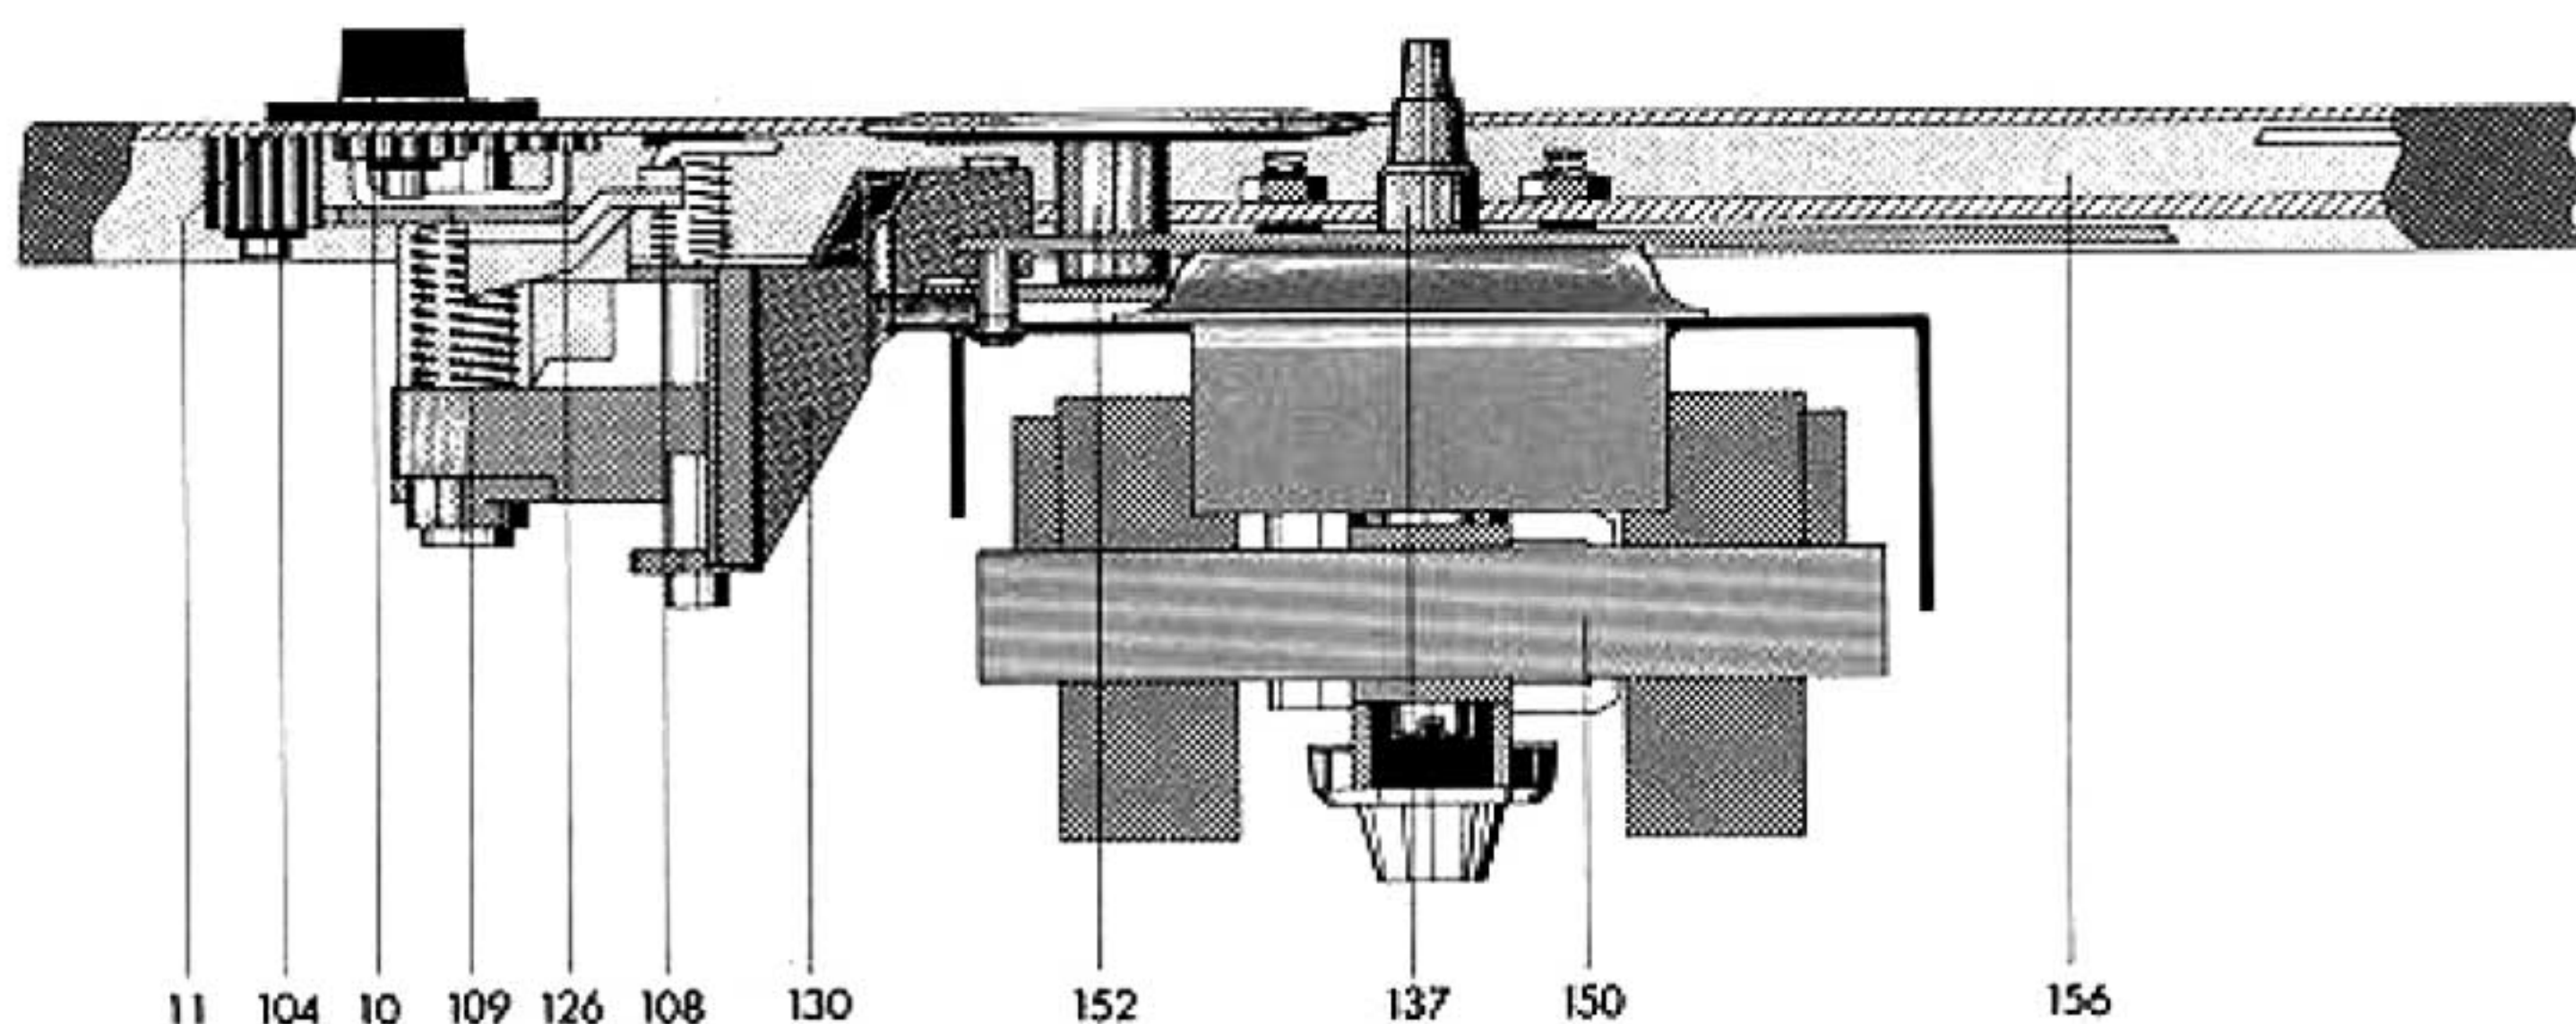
Motoraufhängung und Antrieb des Plattentellers Dual 1222
